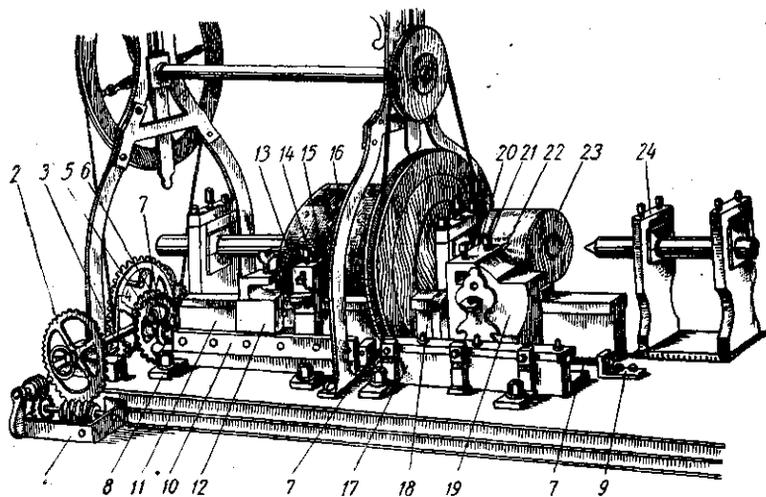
Сунорт большого токарно-контрольного станка Нартова 1718—1729 гг.
